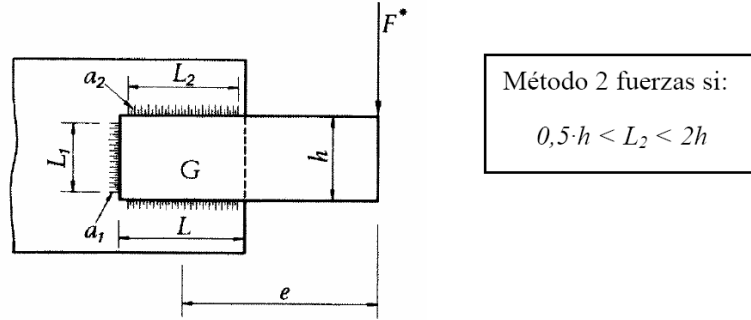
DOS SOLDADURAS FRONTALES Y UNA LATERAL SOMETIDAS A TORSIÓN Y CORTANTE
